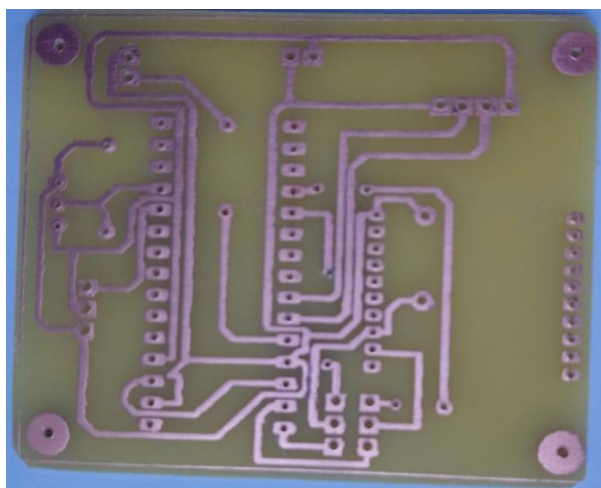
Placa electrónica *Printed Circuit Board* (PCB)
